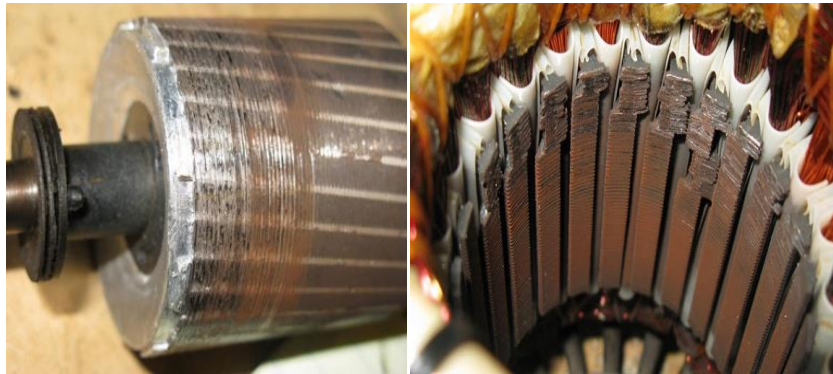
Exemple de dégâts au stator et rotor dus au défaut de roulement d'un moteur asynchrone.
